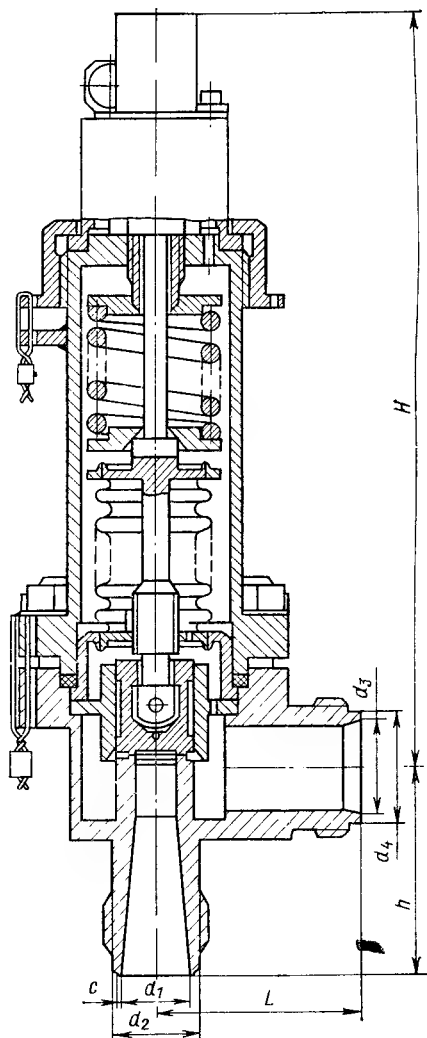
Предохранительный сильфонный клапан А 55061 на $p_p = 0,26$ МПа.
